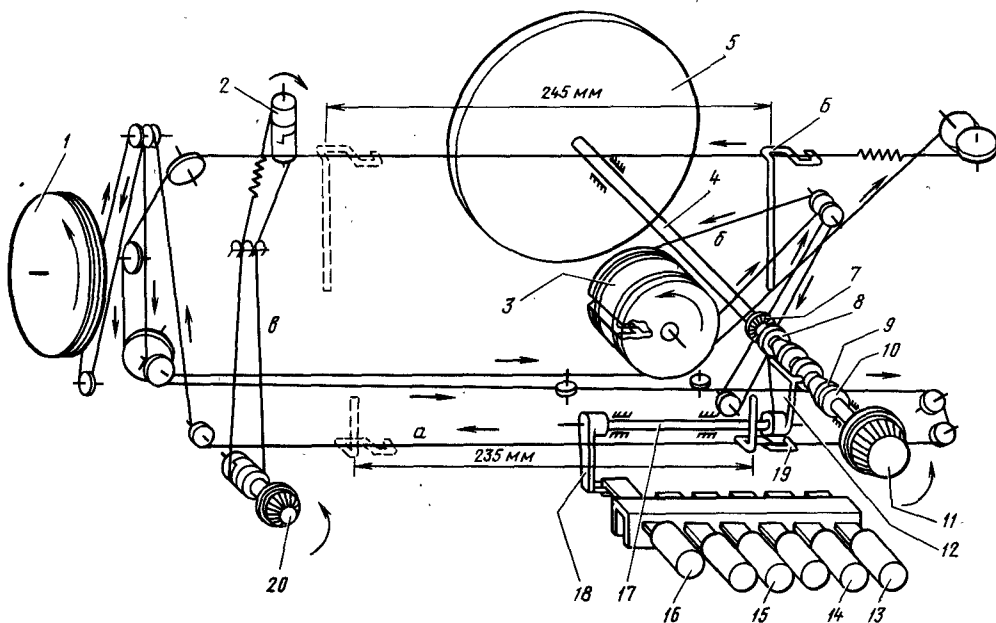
Кинематическая схема верньерного устройства РПУ:
